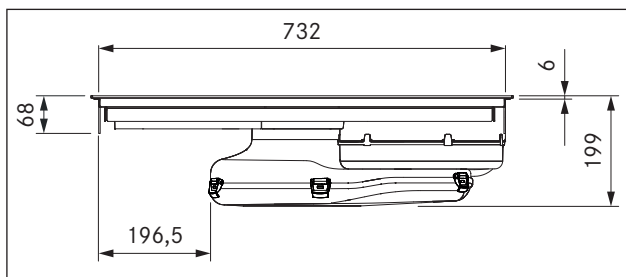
PURA dimensioni apparecchio vista frontale
